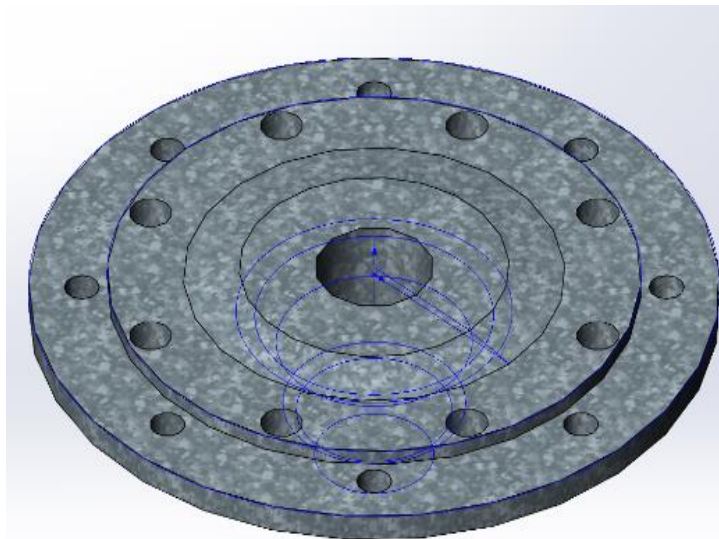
3Д-модель деталі “Ступиця”
